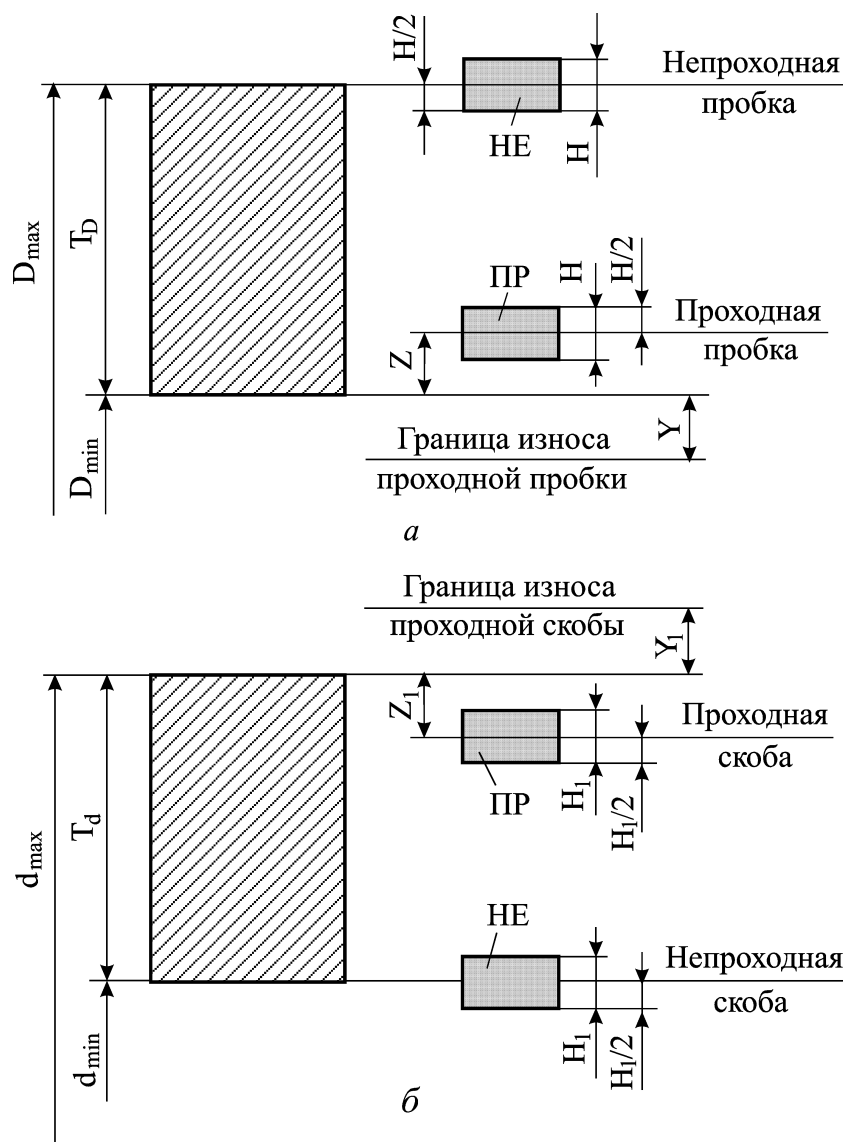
Схемы расположения полей допусков гладких калибров для контроля отверстий (а) и валов (б) с номинальными размерами до 180 мм и допуском изготовления по IT6-IT8
